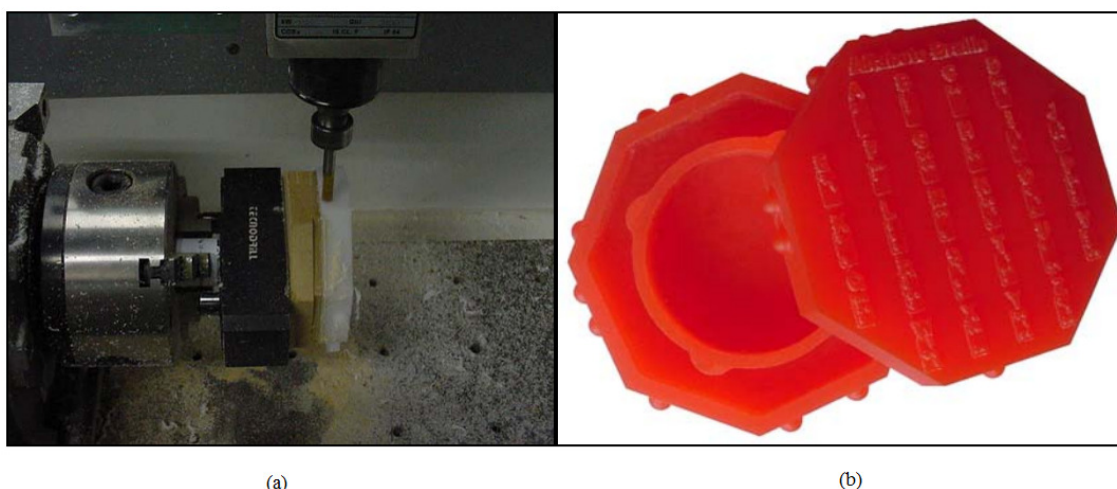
a) Ferramenta de usinagem (fresa) b) Protótipo usinado em PU
